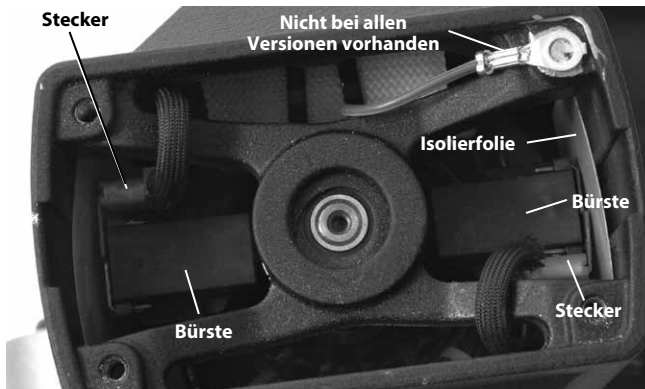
Platzierung der Bürsten - Motorabdeckung entfernt
